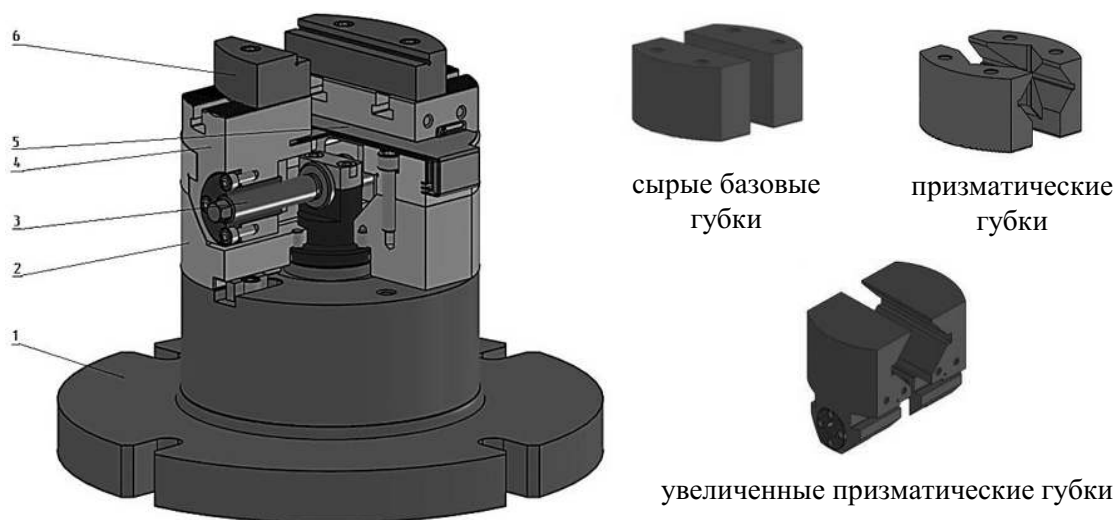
3D-модель приспособления и комплект сменных губок:
